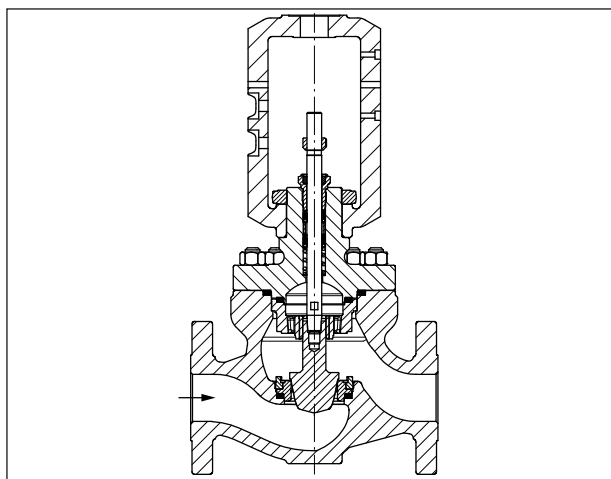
Durchgangsventil Typ 251GR mit geschraubtem Sitz
